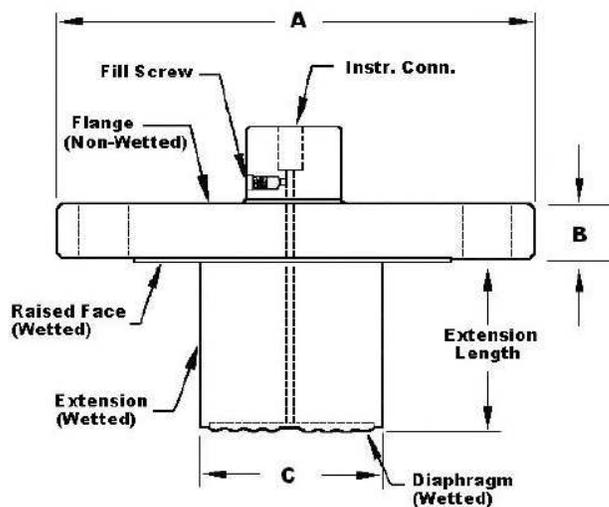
Dimensiuni Flanse (Diafragme cu Extensie)
